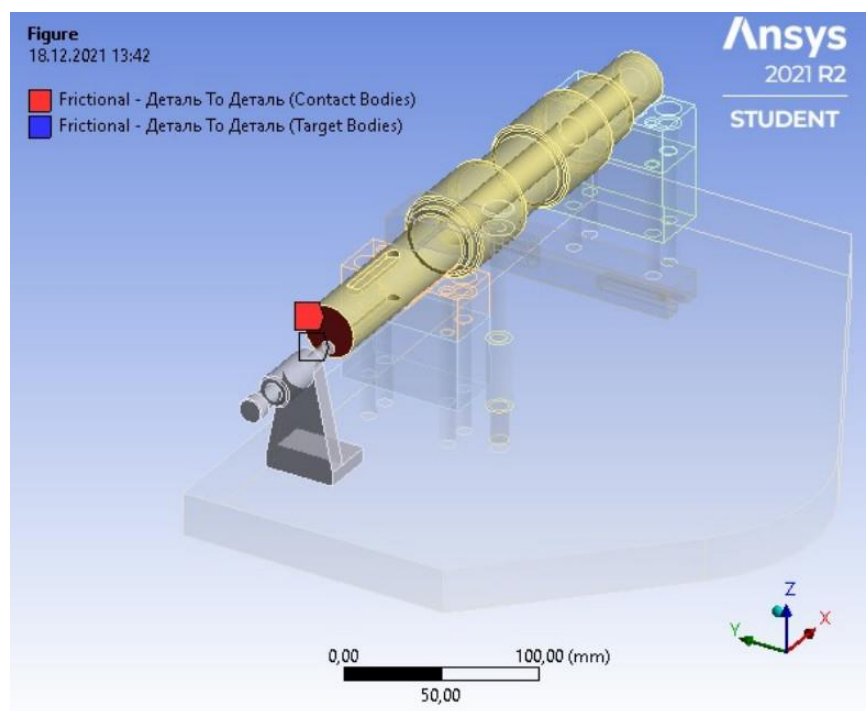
Сполучення між поверхнею заготовки та упору
